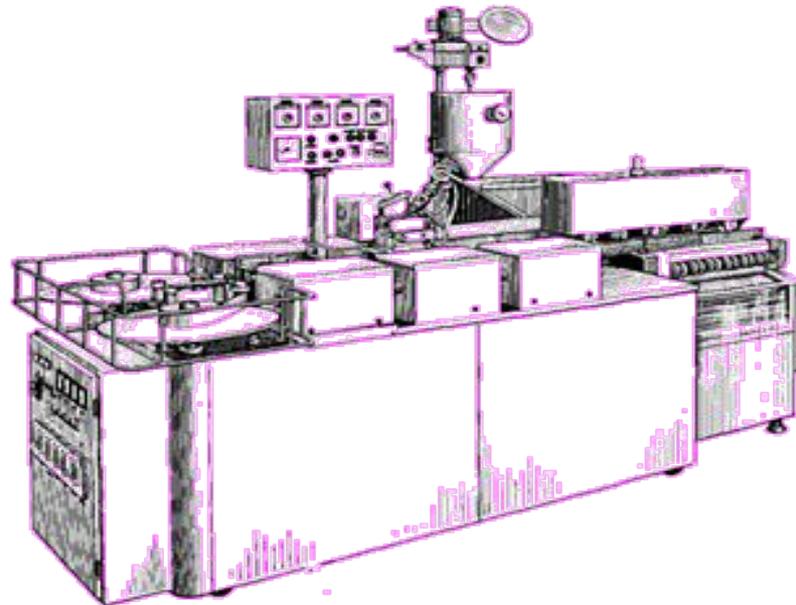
Внешний вид автомата «Стрелас-200S» для выливания и упаковки свечей.
